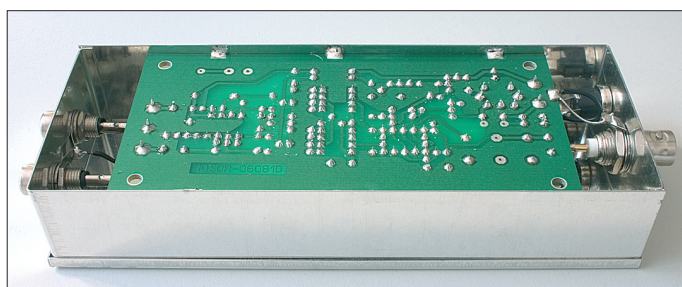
Ansicht eines fertig aufgebauten Kits von unten; deutlich erkennbar sind die Löt pads zur Befestigung der Platine am Weißblechgehäuse
